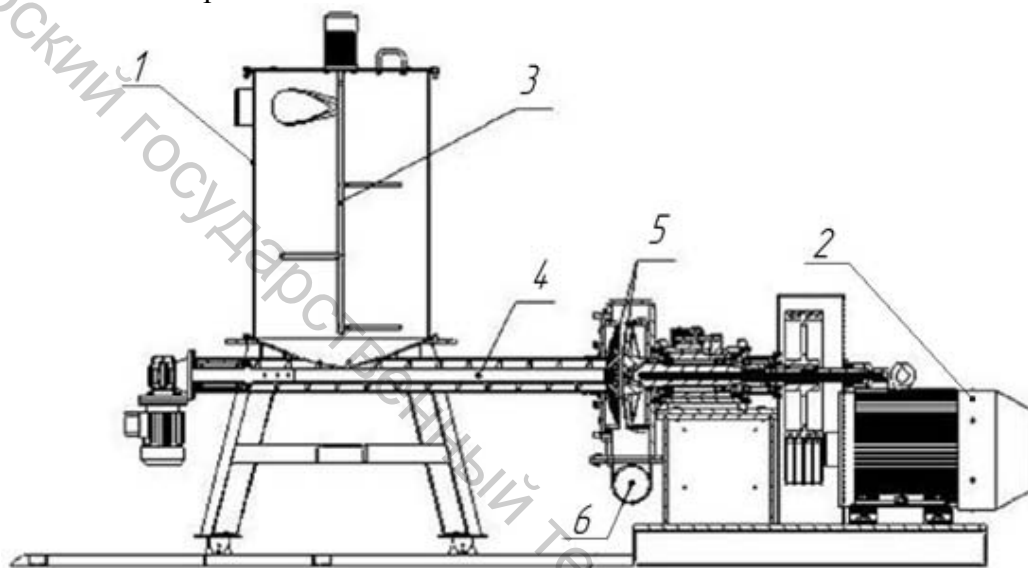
Внешний вид пласткомпактора в разрезе:
